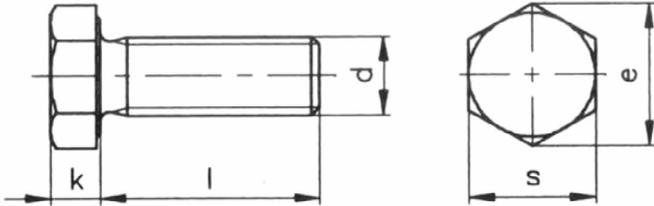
| Tornillo hexagonal DIN933 | Fuente: DISLA
